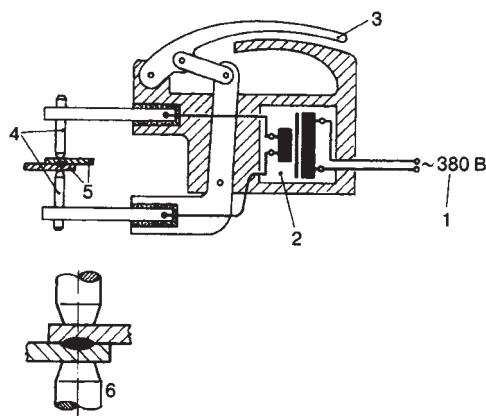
Принципова схема кліщів для контактнo-точкового зварювання і зварна точка:
